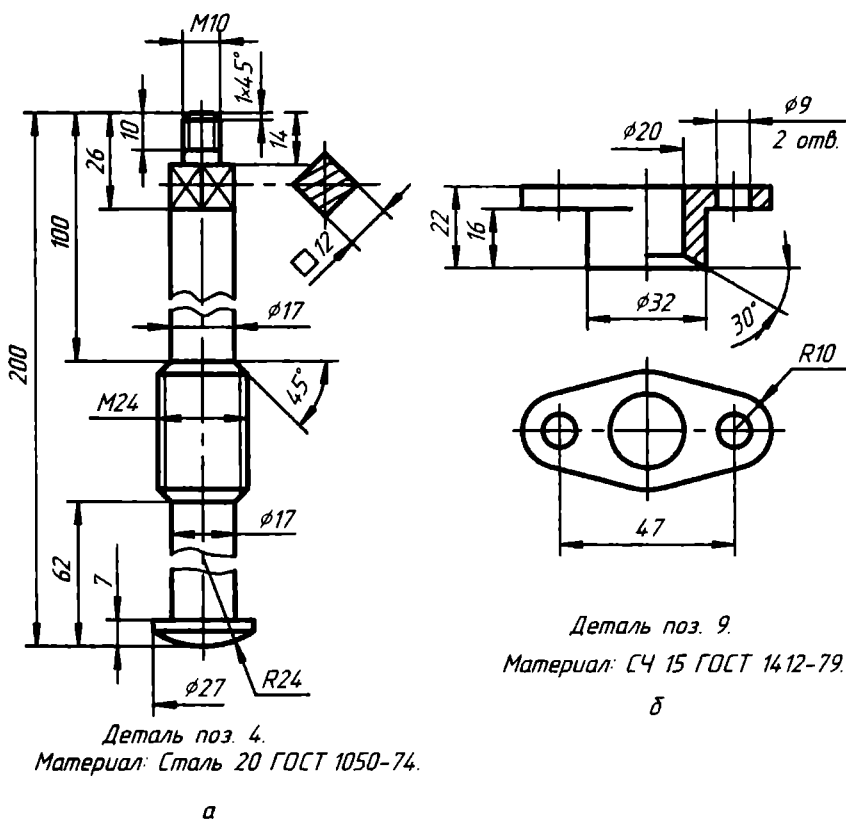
Чертежи: а — шпинделя; б — фланца
